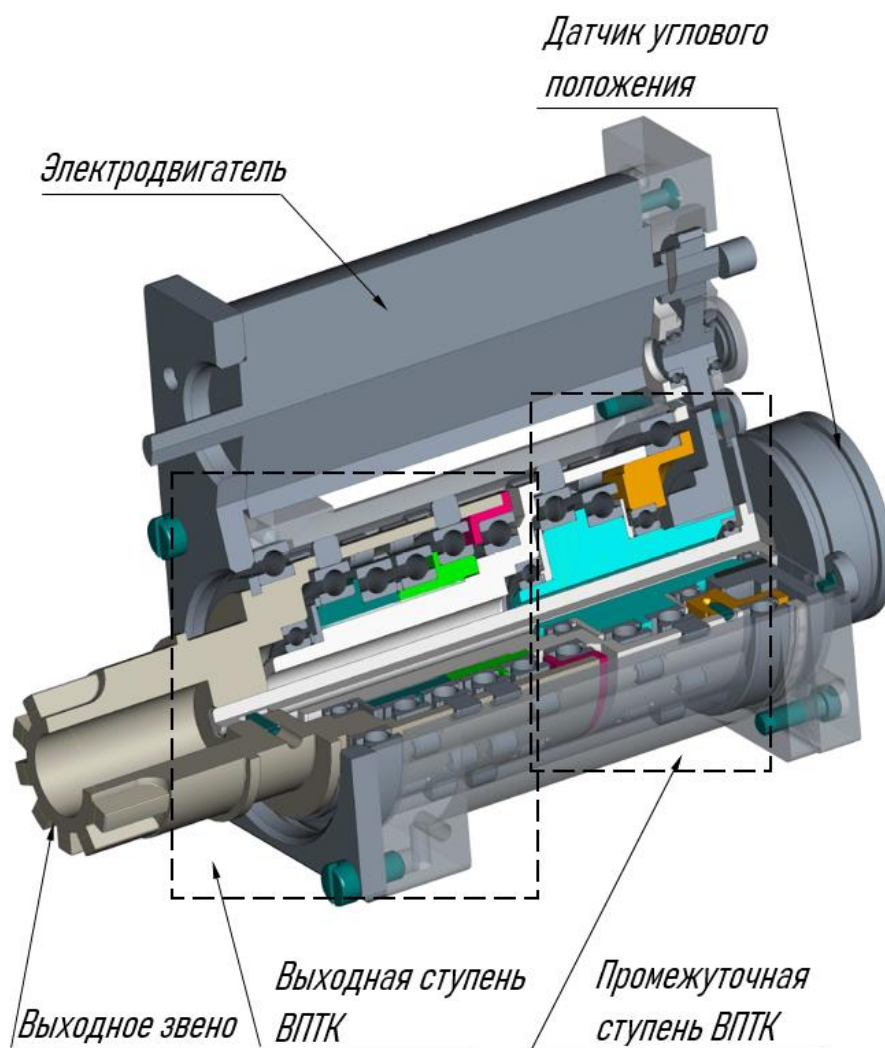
ИМ на основе двухступенчатой ВПТК и промежуточного цилиндрического редуктора
